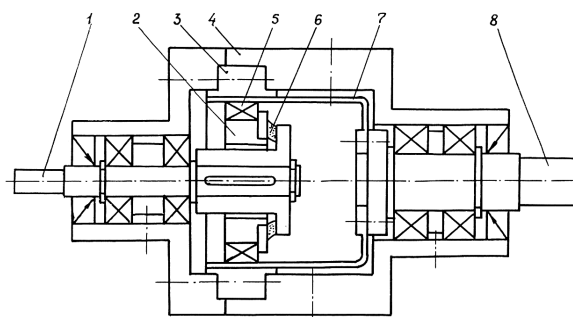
Конструктивная схема волнового редуктора фирмы VSM:
